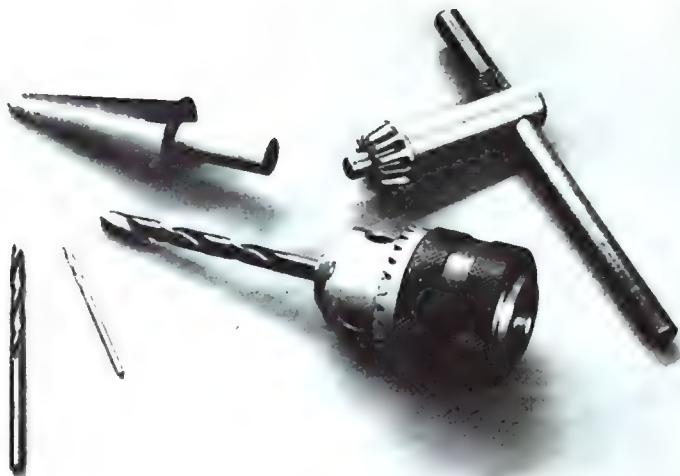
Ein von der Elektrobohrmaschine abgeschraubtes Dreibackenfutter dient beim Kunststoffbohren als Halter zum Bohren mit der Hand.
